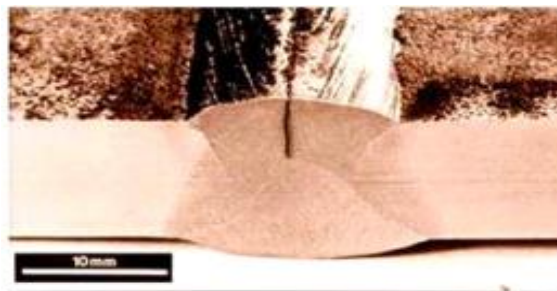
Fissuration à chaud dans la zone fondue [15].
